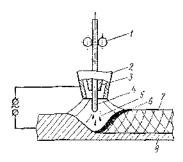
Схема автоматической и полуавтоматической аргонодугозой сварки илавящимся электродом
